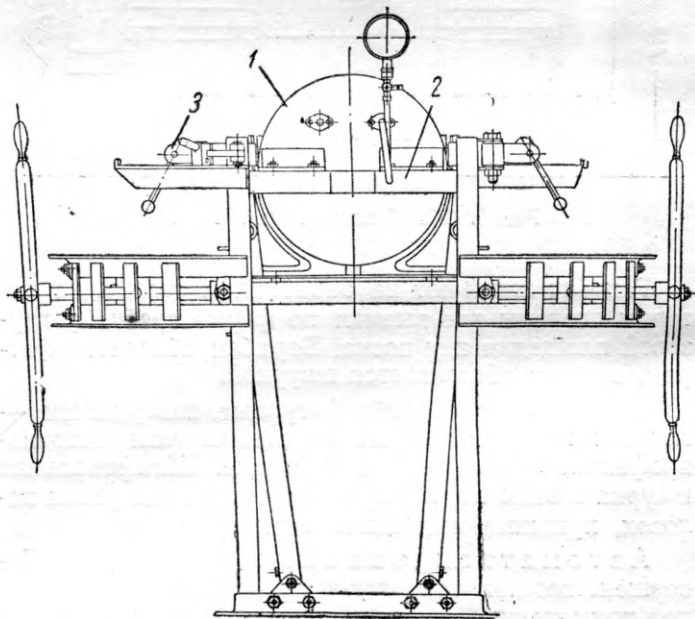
Общий вид гнутарно-сушильного станка ЛЫГ
